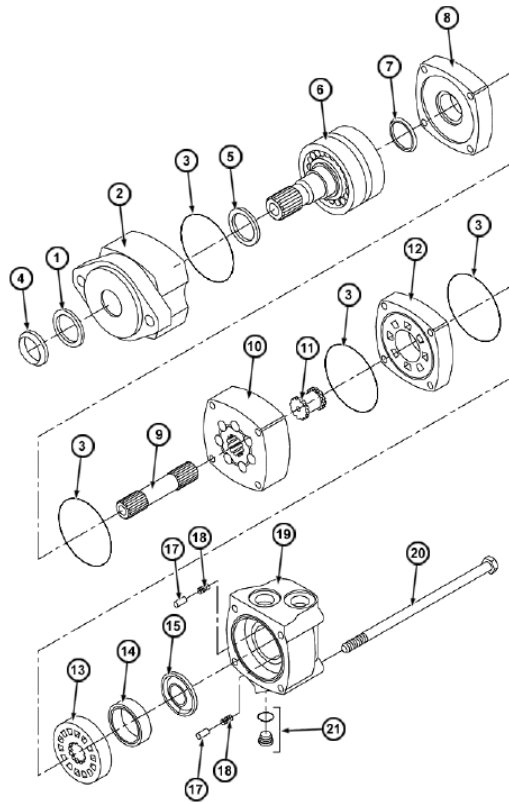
Vista Explosionada del Motor del Rodillo Tumbador [1].
